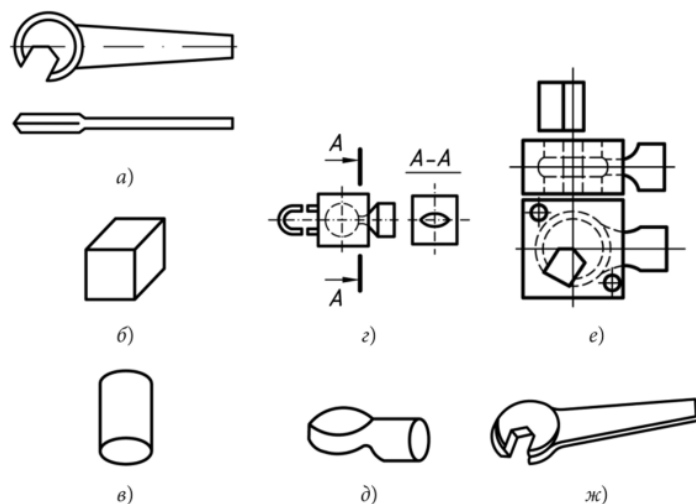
схема переходов при изготовлении поковки гаечного ключа:
